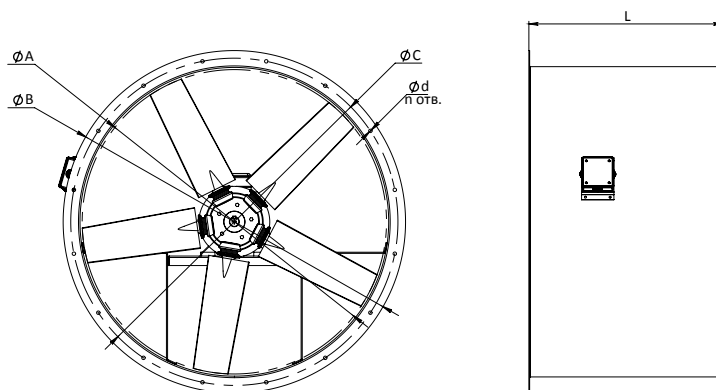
Габаритные размеры вентилятора в исполнении корпуса «Н»
